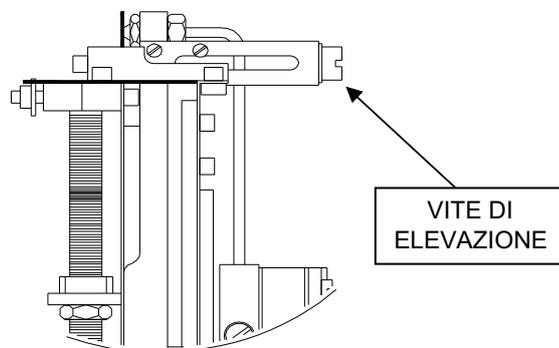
DISPOSITIVO DI ELEVAZIONE
